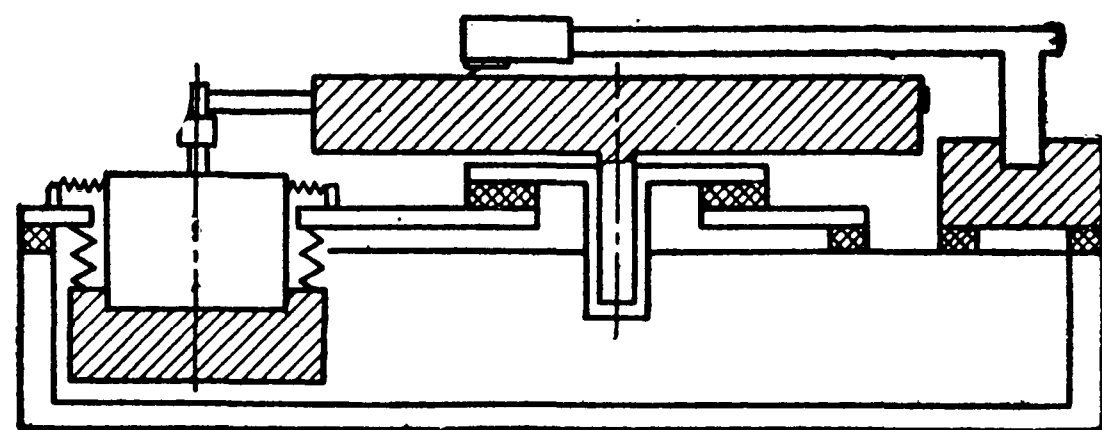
Схема движущего механизма проигрывателя с элементами защиты от вибраций.
